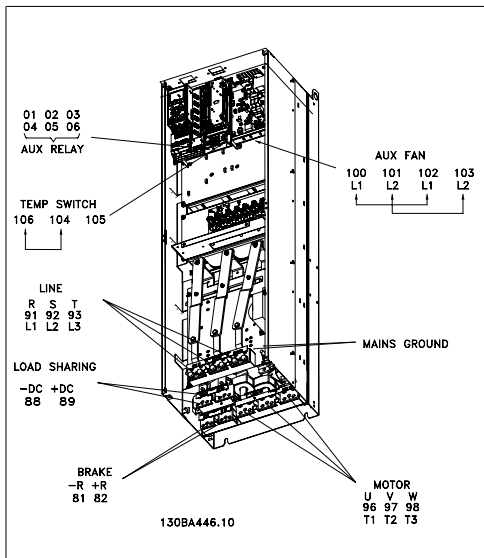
Compact IP 00 (Шасси), корпус D3
